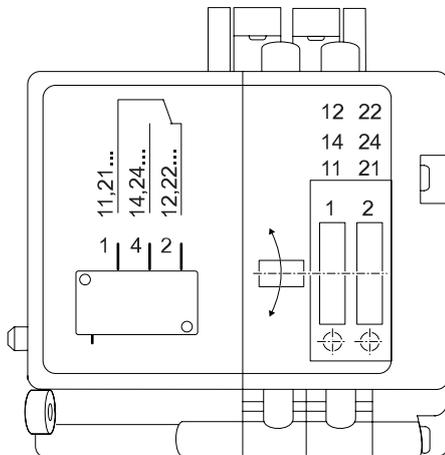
Final de carrera de engranajes giratorio de 2 pasos
